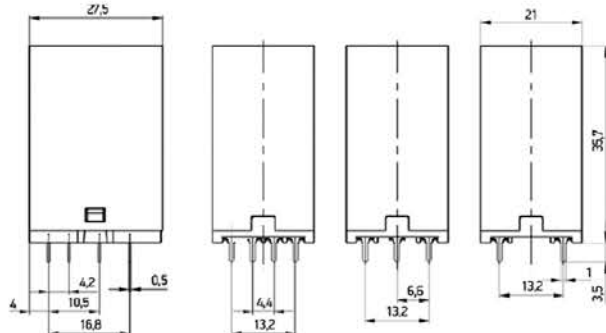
Габаритные, установочные, присоединительные размеры реле OptiRel G RP55-1X для монтажа на печатную плату
